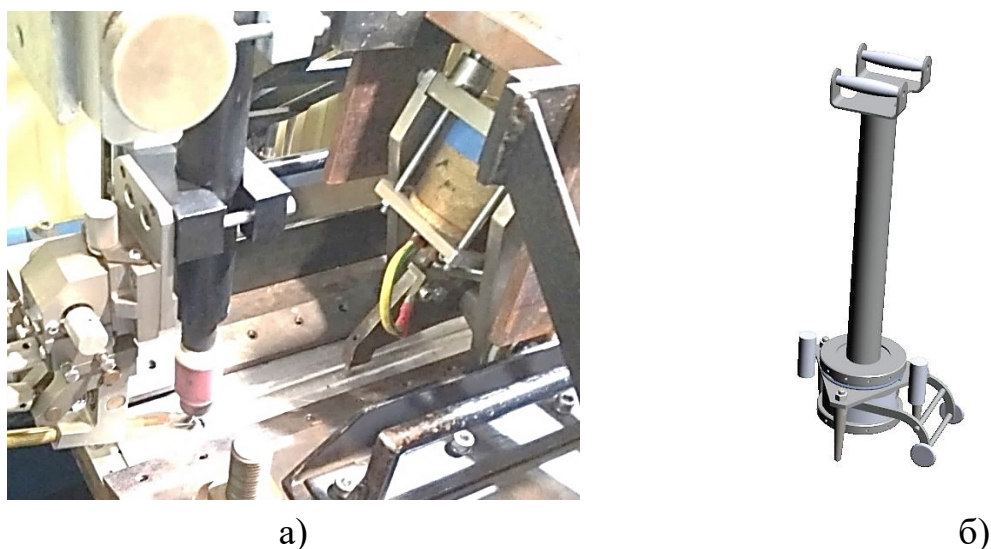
Процес ЕДО зварних пластин з використанням а) напівавтоматичного пристрою, б) ручного пристрою є
